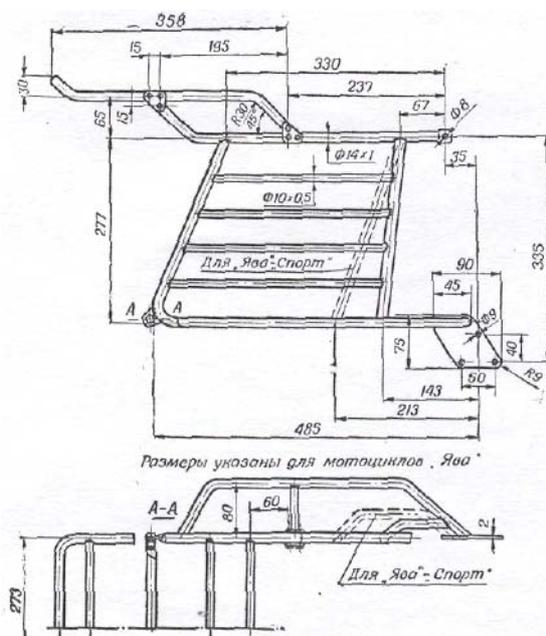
Чертеж багажника с боковыми и задней грузовыми площадками
